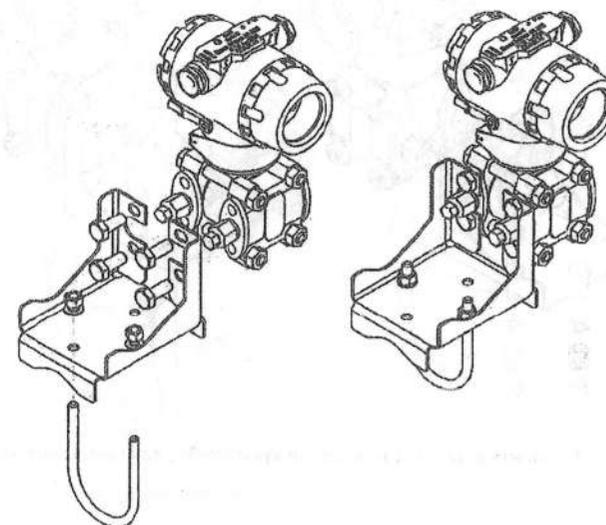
Монтаж датчика на угловой кронштейн, для крепления на трубе (B04)
